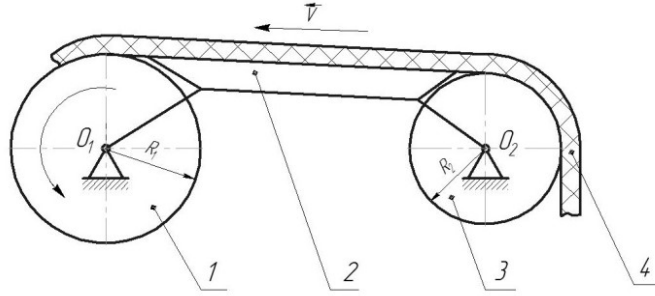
Схема транспортирующего устройства: 1 – ведущий вал; 2 – расправочный стол; 3 – ведомый вал; 4 – кожаный полуфабрикат
